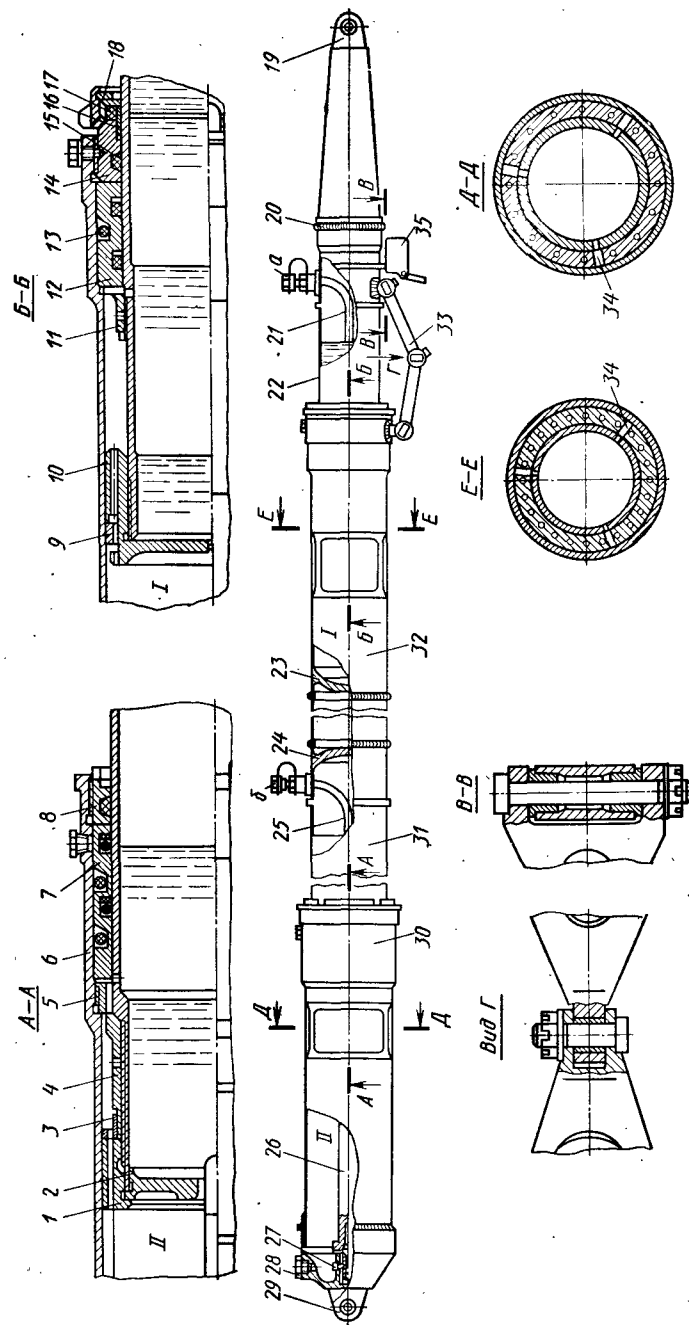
Конструкция двухкамерного жидкостно-газового амортизатора главной стойки шасси:
